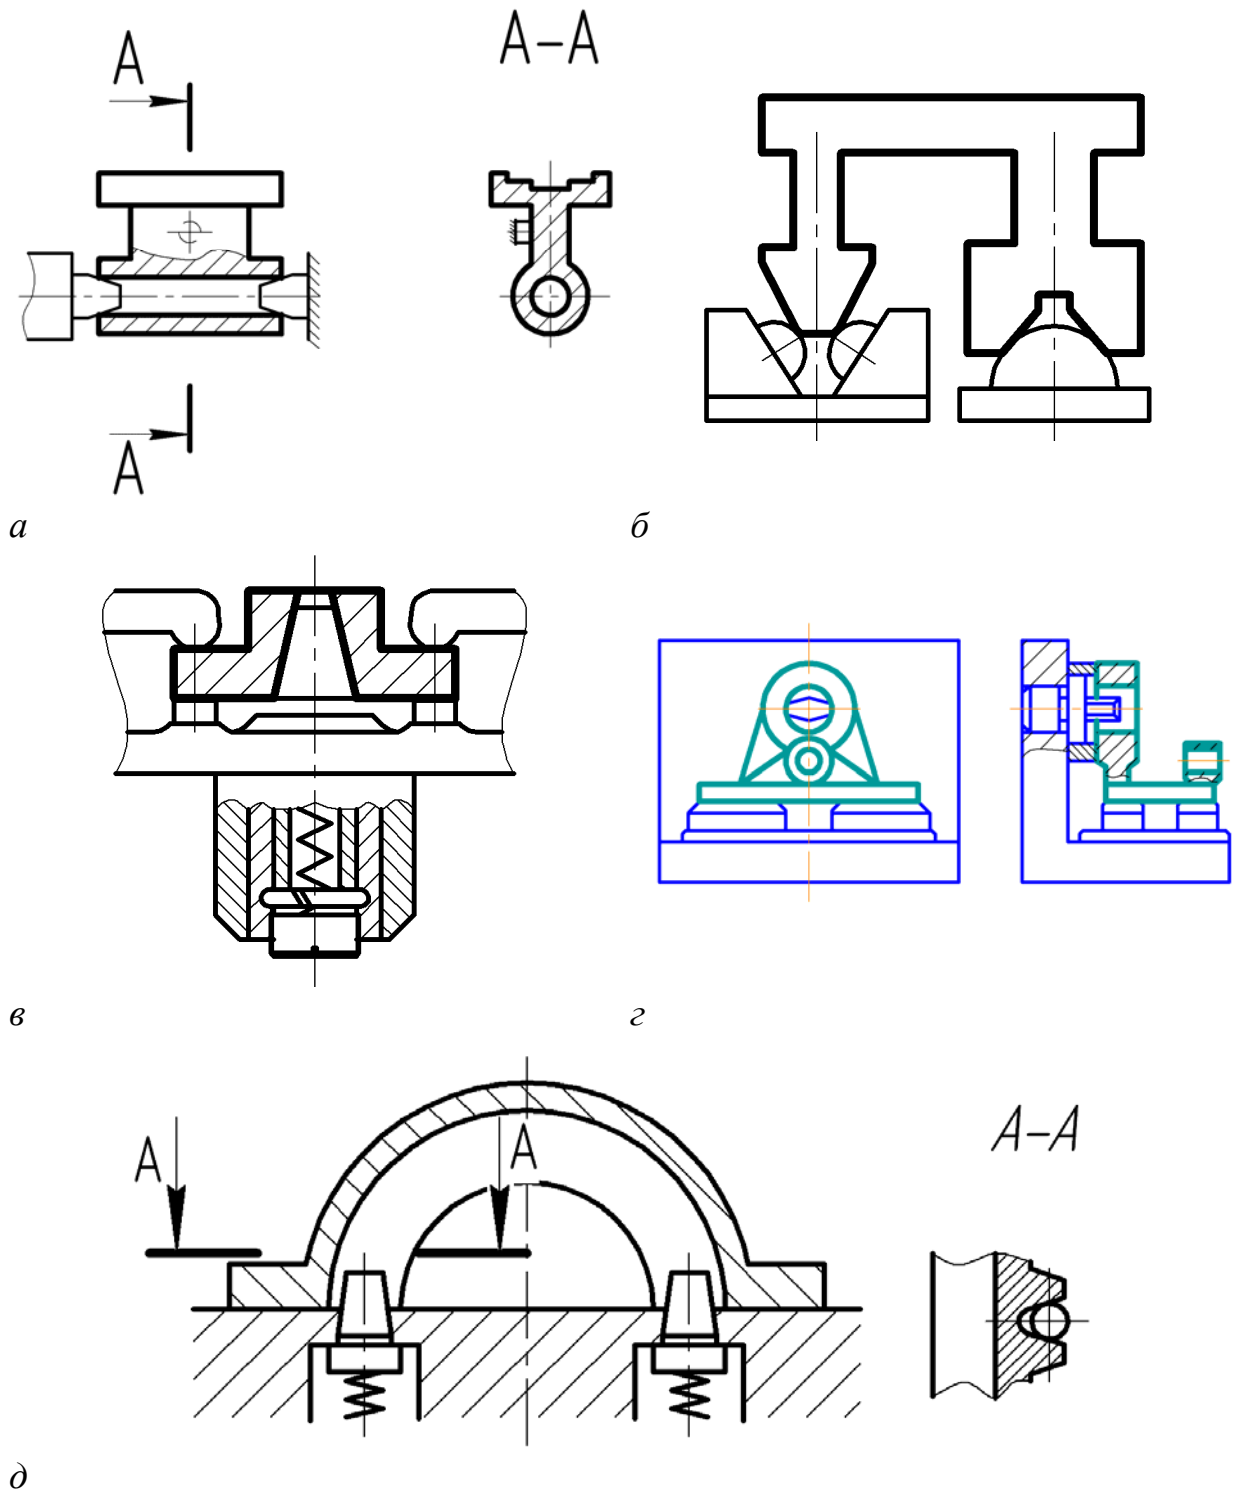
Комбинированные схемы установки корпусных деталей:
